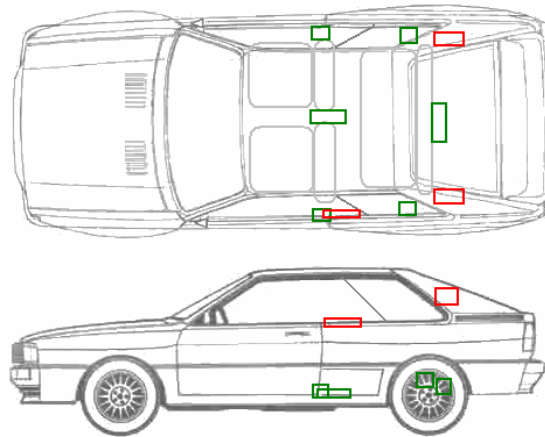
Gurtbandführung durch die Karosserie in den Radkasten [22]
